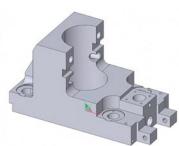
Anwendungsbeispiel für eine schweißtechnische Reparatur eines Stempelhalters für eine Hatebur-Presse
